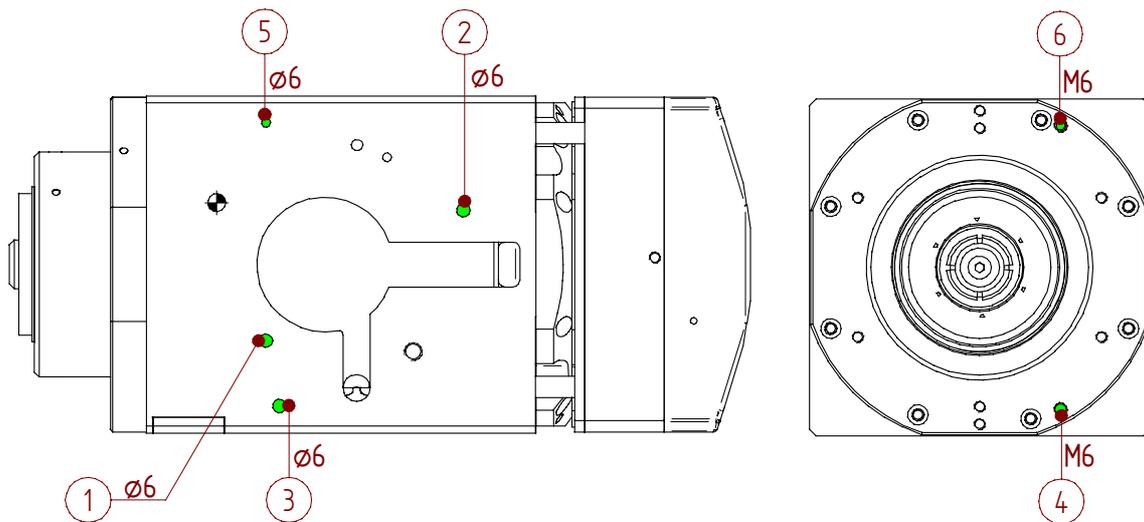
hydraulische anschlüsse für ES779 mit Befestigungsnuten
